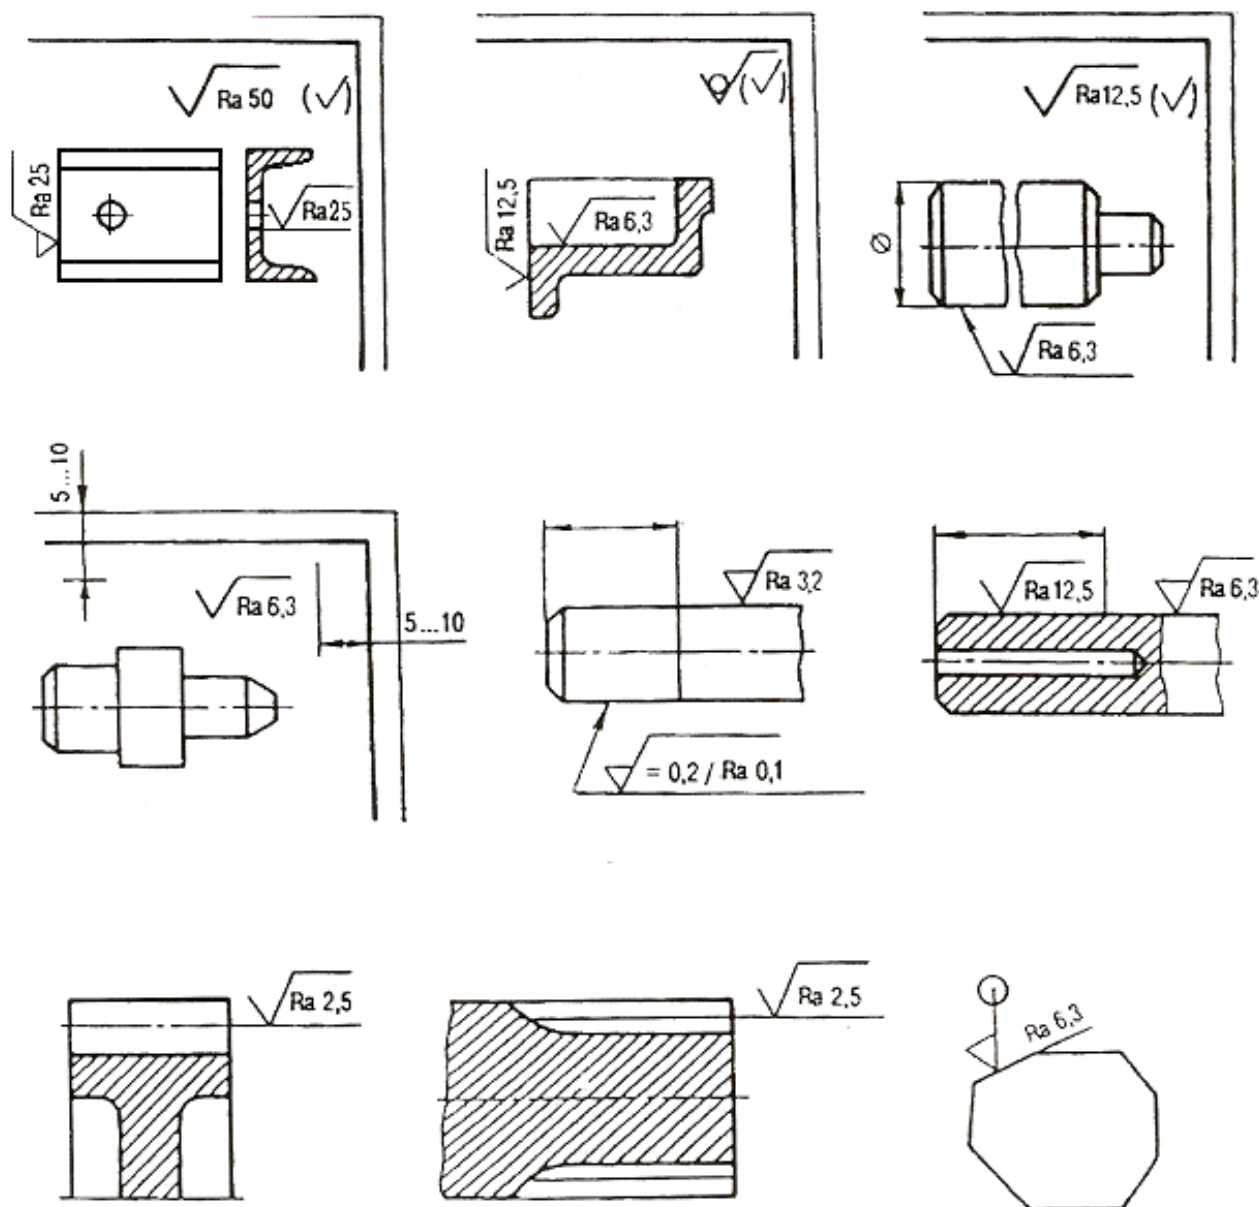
Примеры обозначений шероховатости поверхностей
